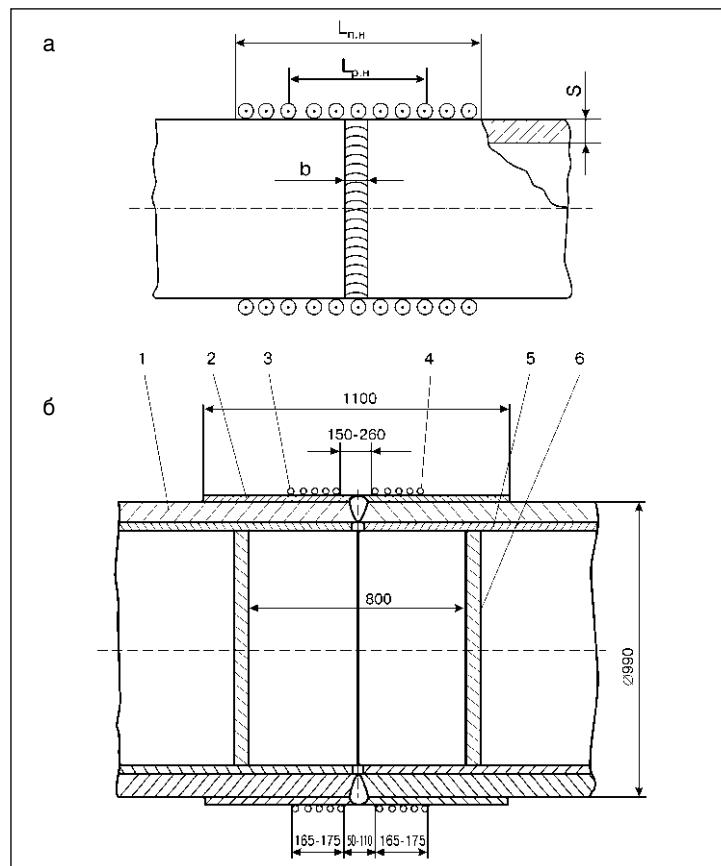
Зоны полного $L_{п,н}$ и равномерного $L_{р,н}$ нагрева при термообработке: а — типовая схема установки (в — ширина шва); б — схема установки индуктора при термообработке стыков труб ГЦК 5-го блока Воронежской АЭС с реактором ВВЭР-1000 (1 — сварное соединение; 2 — наружная изоляция; 3 — первая секция индуктора; 4 — вторая секция индуктора; 5 — плакирующий слой; 6 — внутренняя теплоизоляционная перегородка)
